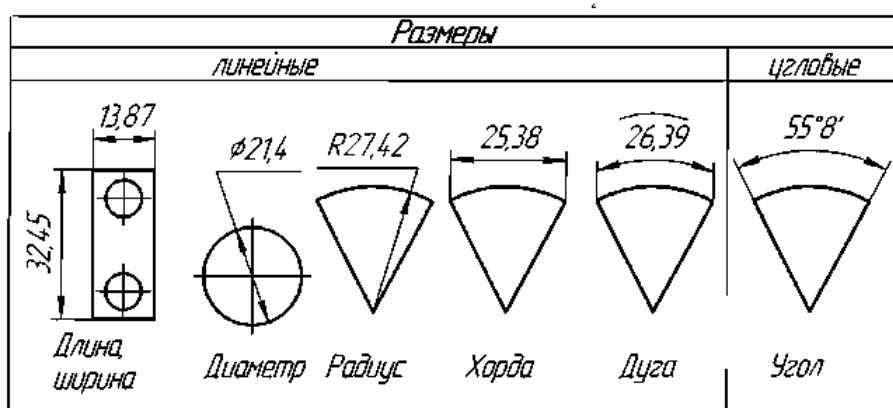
Примеры обозначения линейных и угловых размеров
